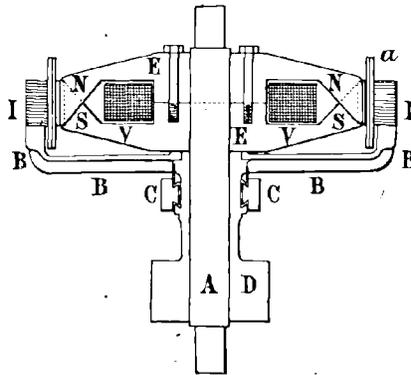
Coupe du moteur Joël par un plan parallèle à l'arbre.
